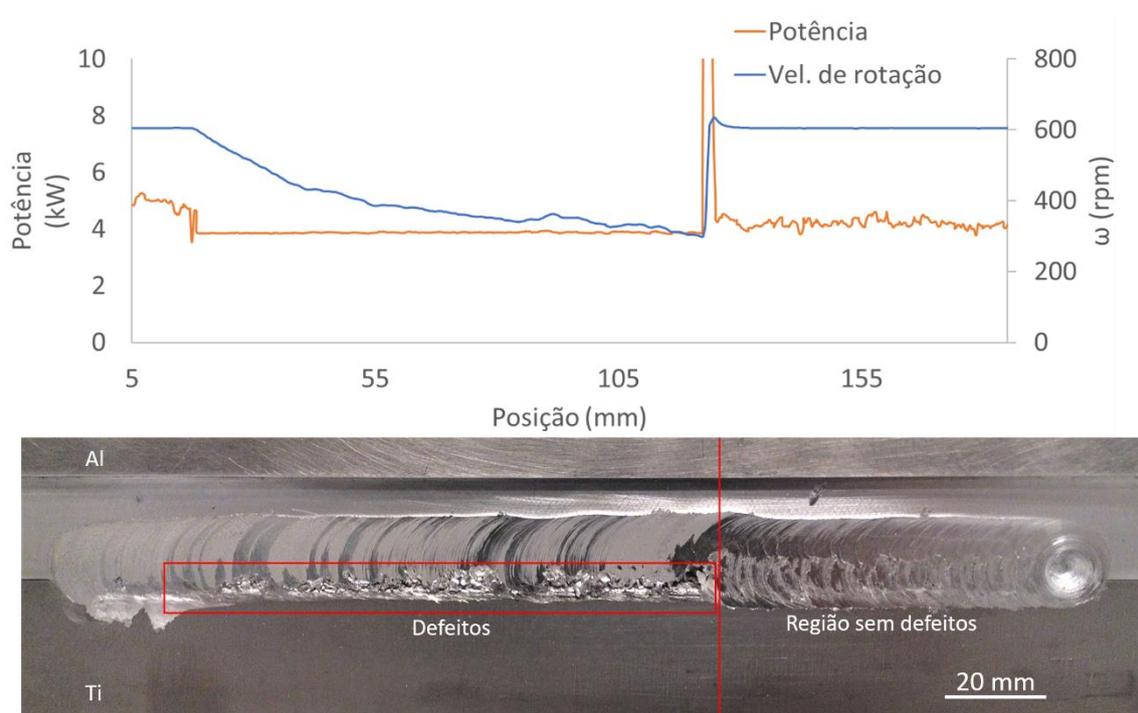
Soldagem das ligas AA7075-T6 com Ti6Al4V. Trecho inicial soldado com controle de potência em 3,9 kW com defeitos na superfície e trecho final soldado com velocidade de rotação constante de 600 rpm sem defeitos na superfície.
